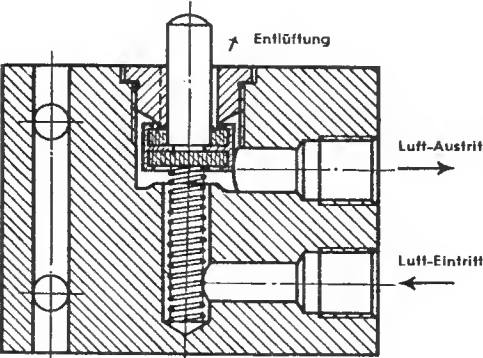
Steuer-Nockenventil, Grundtype 2 für Dreiwegesteuerung
